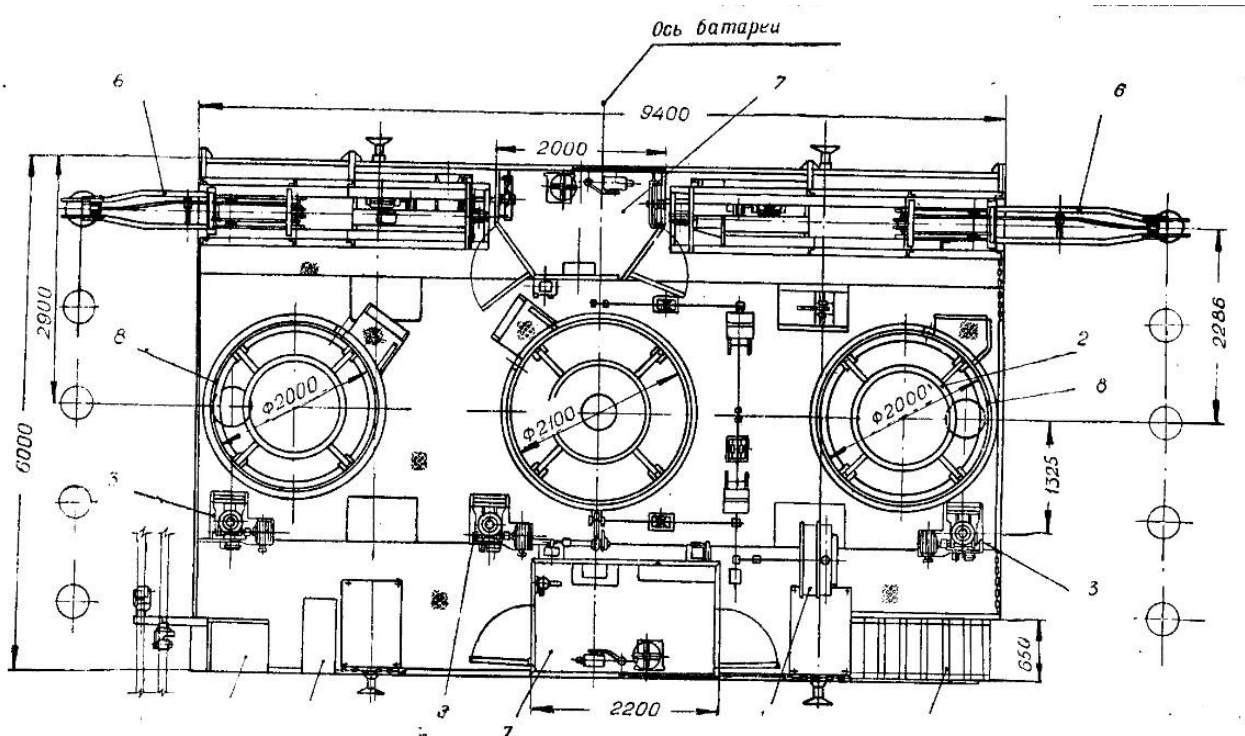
Трьохбункерний вуглезавантажувальний вагон конструкції конструкторського бюро Главмашмета. Вид зверху.
